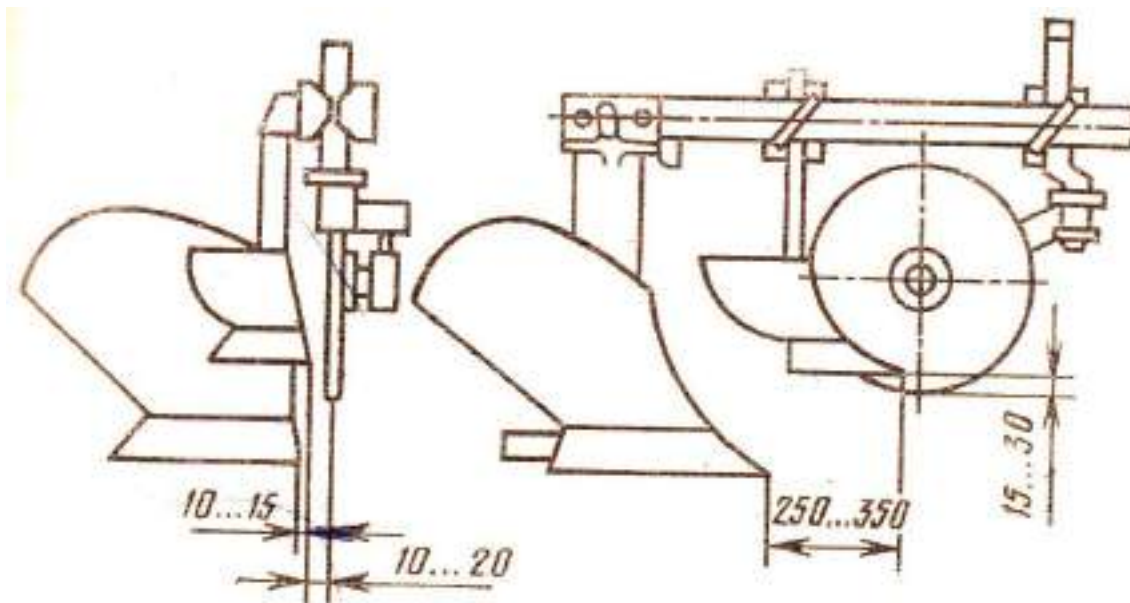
Установка предплужника и дискового ножа относительно корпуса плуга.
